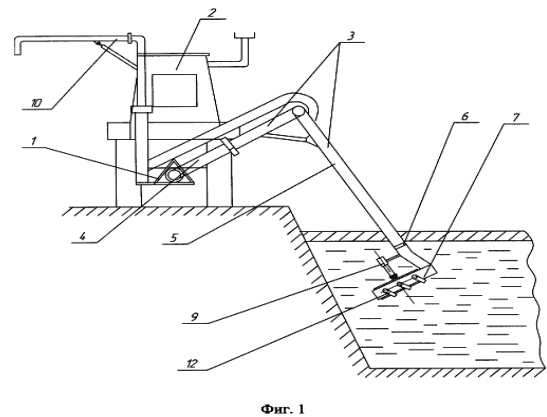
Навантажувач напіврідкого гною: 1-платформа; 2-ковшовий елеватор; 3-направляючий лоток; 4-приймальний лоток; 5-вивантажувальний шнек; 6-гідроциліндр ковшового елеватора; 7-привідний вал; 8-зірочка; 9, 10, 11, 12, 13-пази; 14-пристрій для контролю глибини занурення ковшового елеватора; 15-опора; 16-обмежувач дна похилого елеватора; 17-поперечина; 19-відкіс; 20-стійка; 21-рама.
